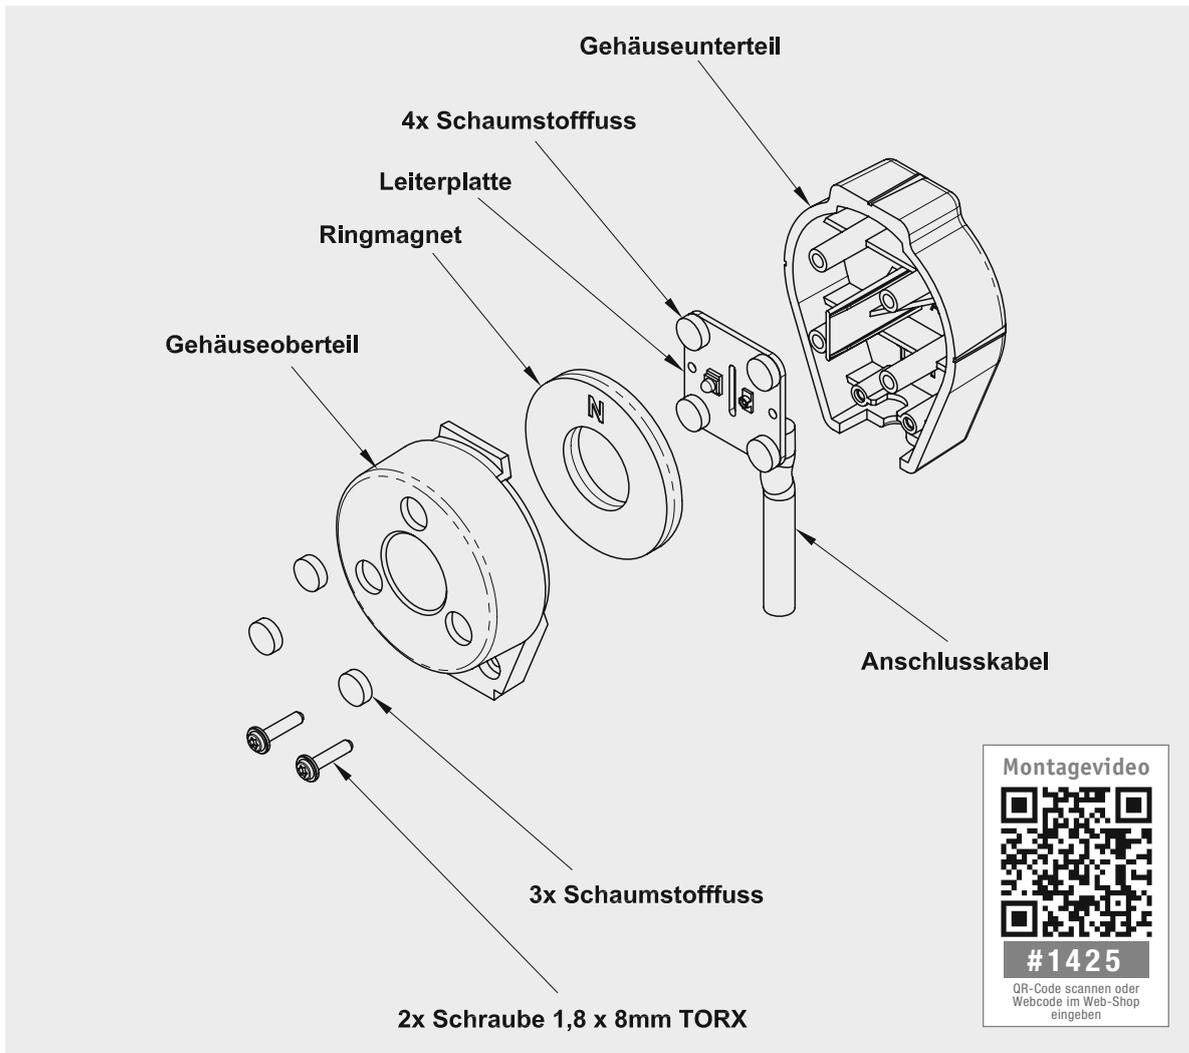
Explosionszeichnung des Auslesekopfes ES-IEC
